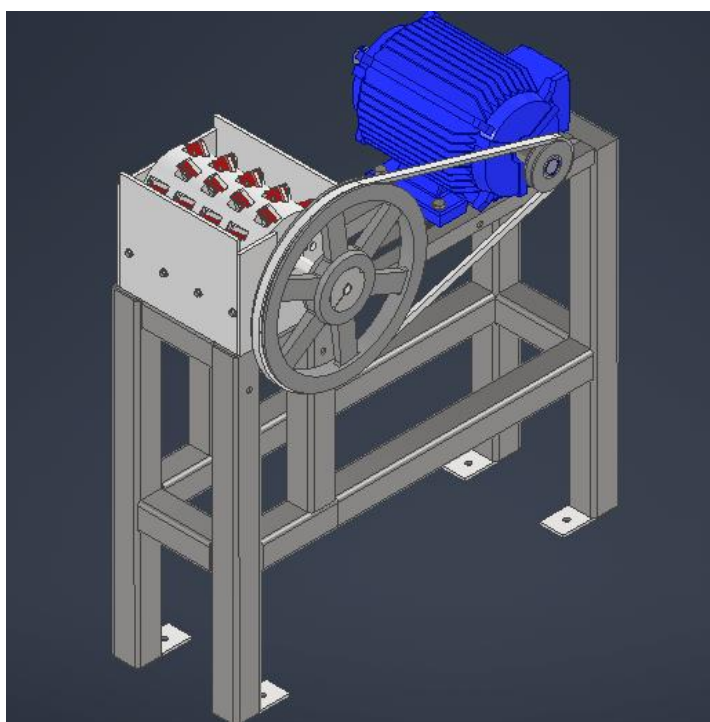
Ensamblaje base-caja-motor-transmisión.
